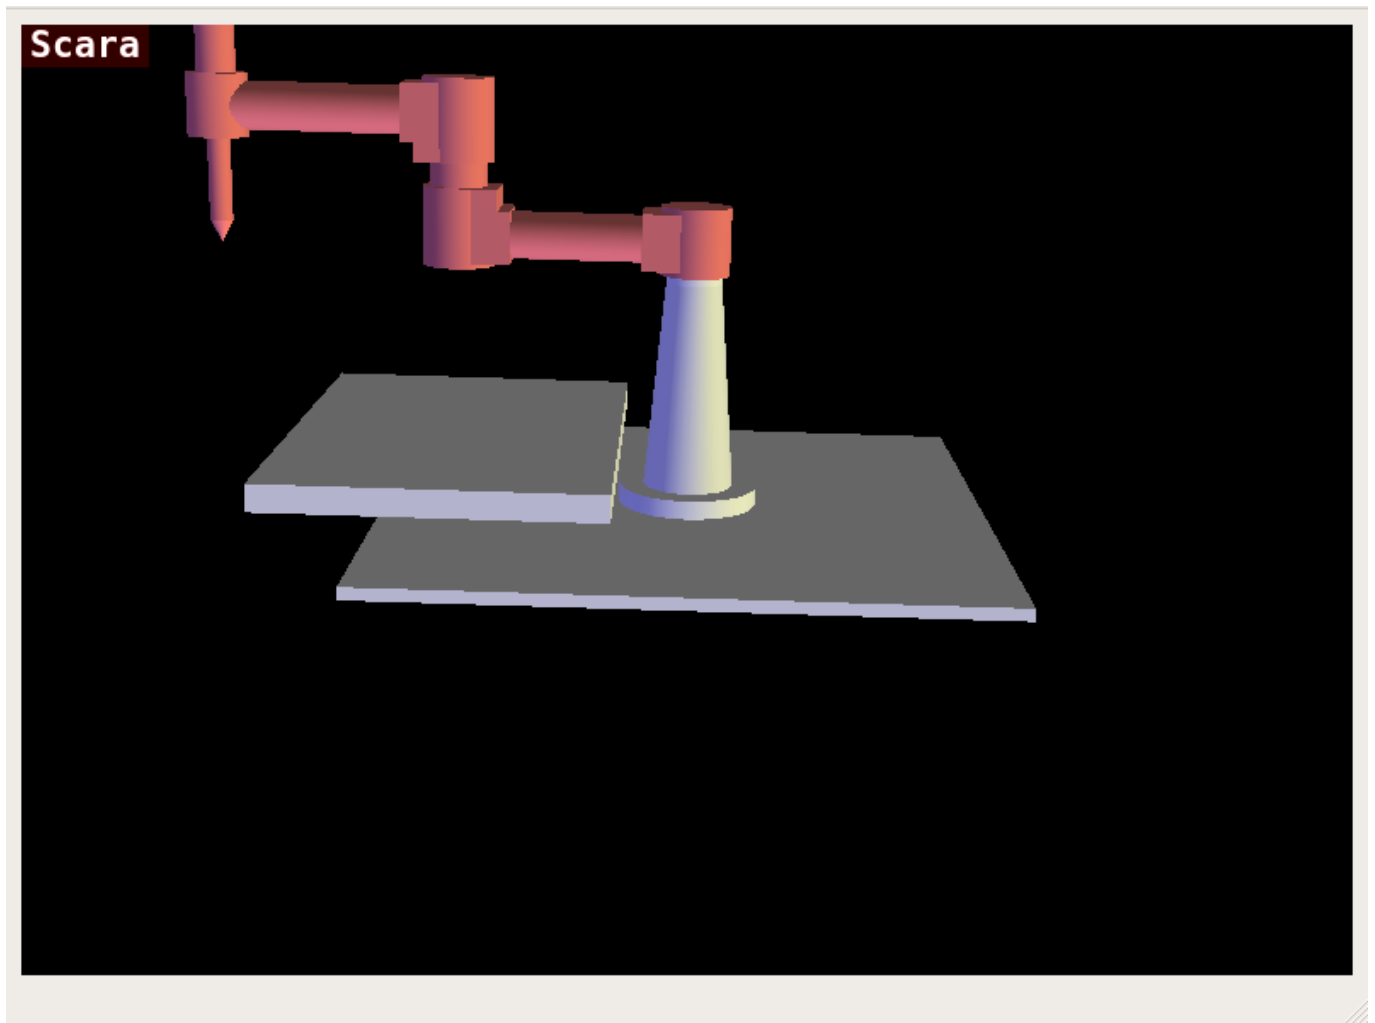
QtVCP vismach\_scara - SCARA Mill 3D View Panel
